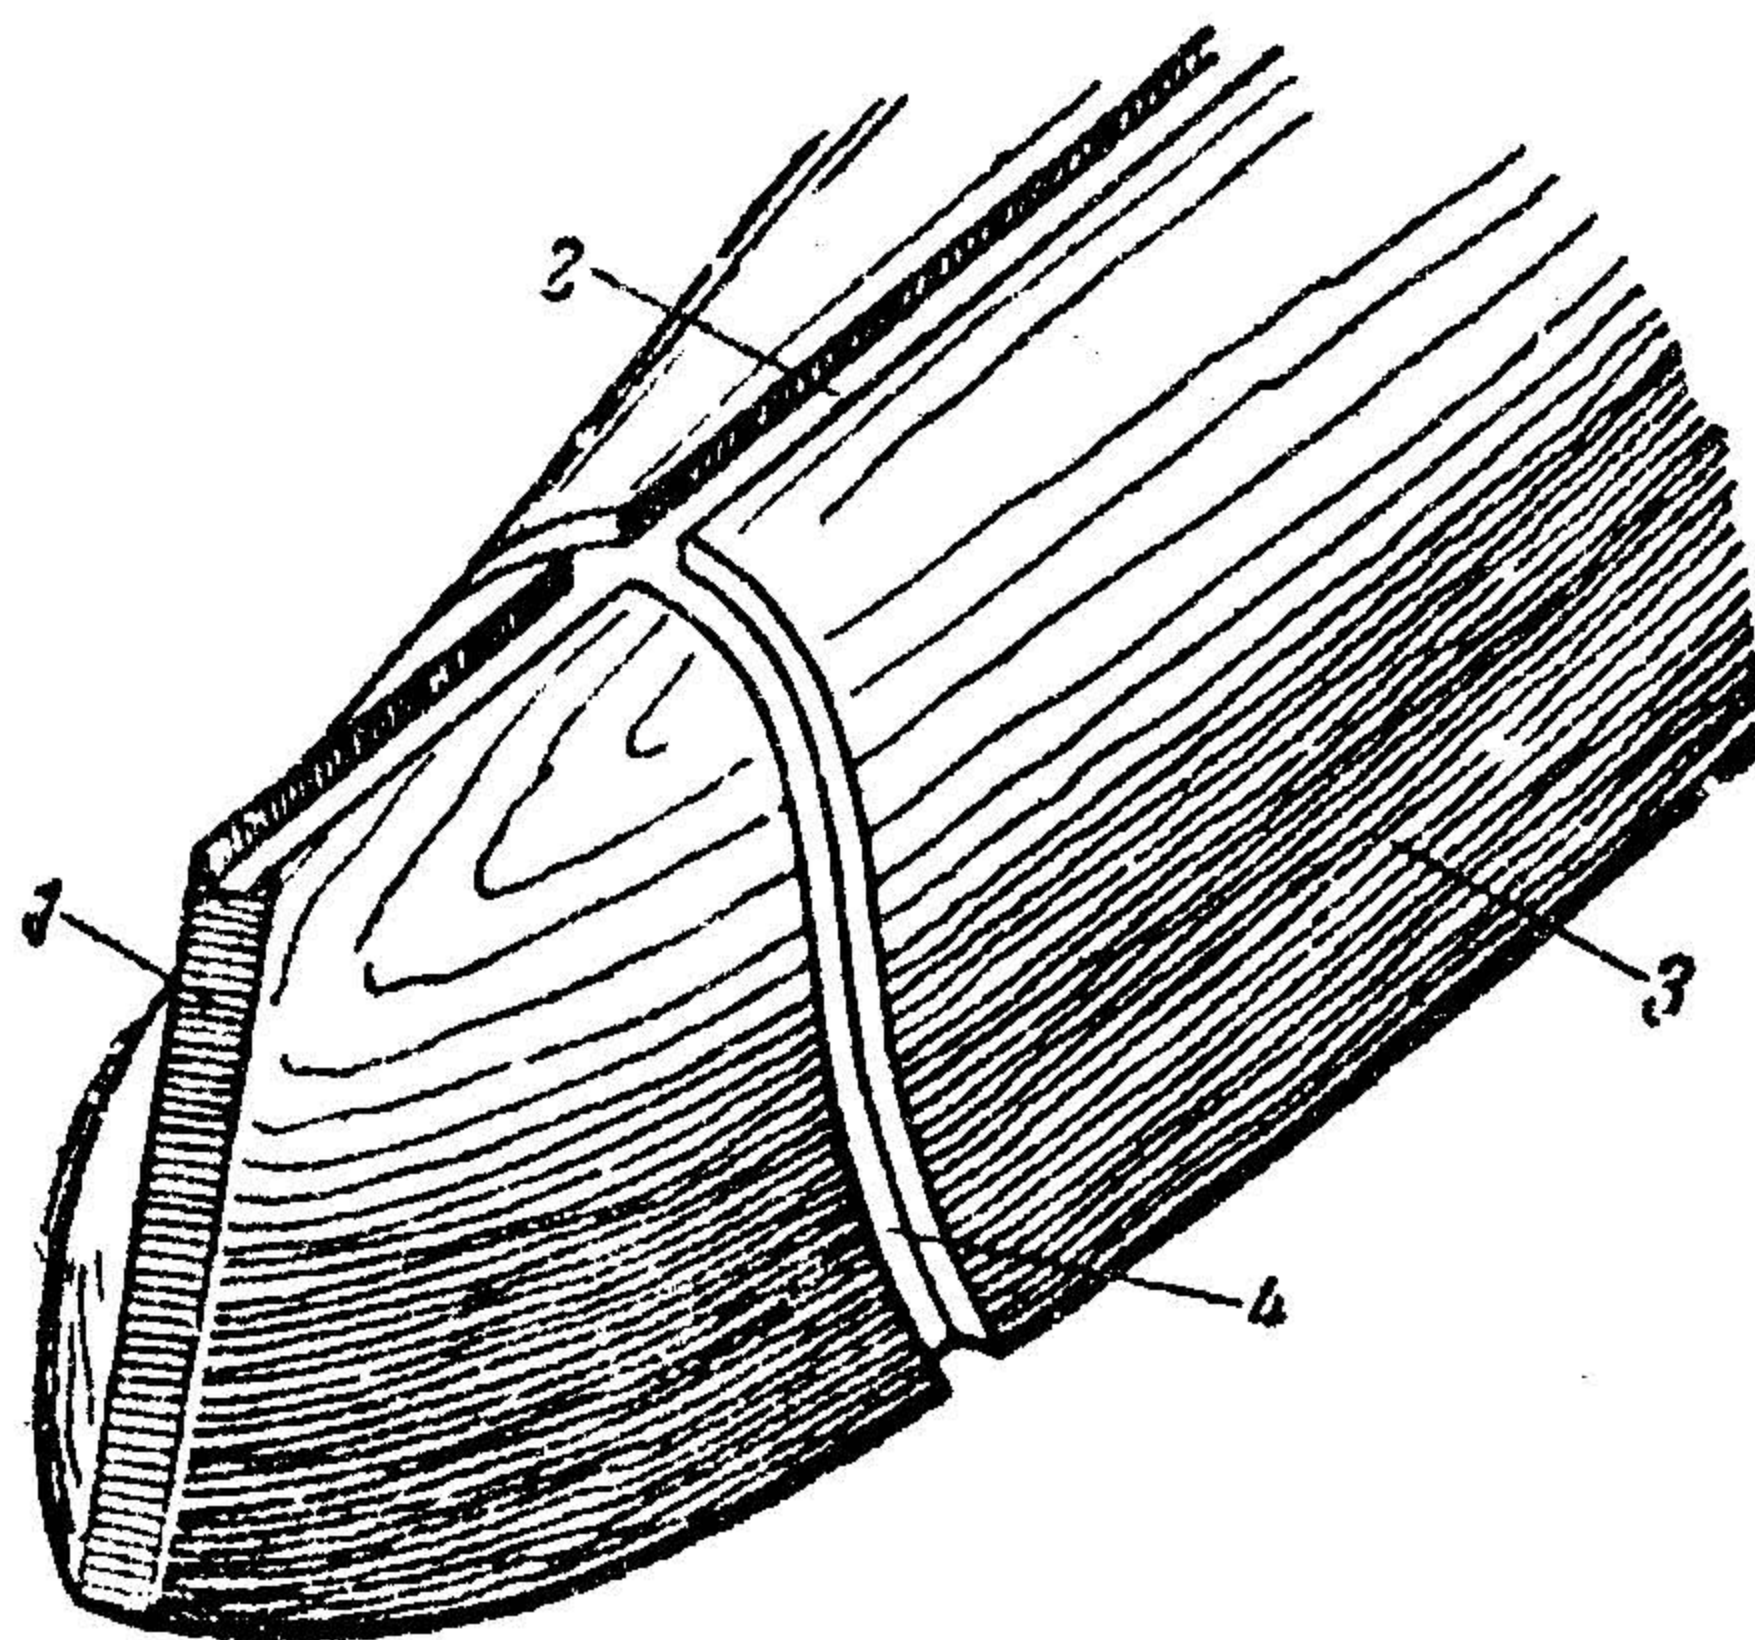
Болванка для обклейки: 1 — срез для носовой бобышки; 2 — продольный паз для киля; 3 — болванка; 4 — поперечный паз для шпангоута
